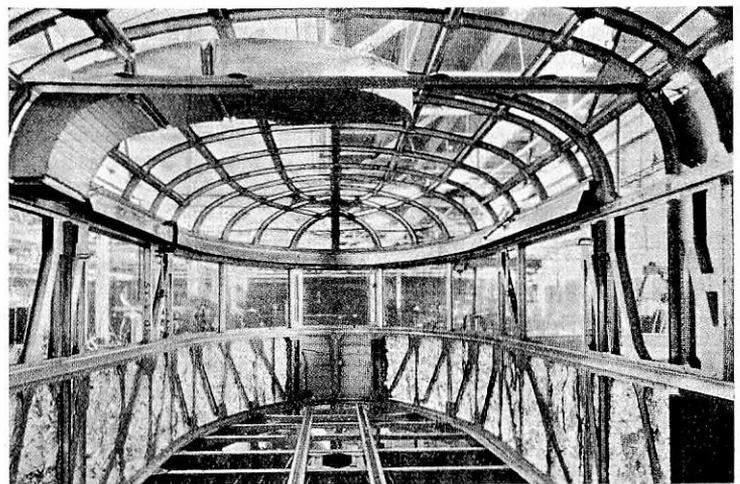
Heckkonstruktion mit Lüftungseinbau.
